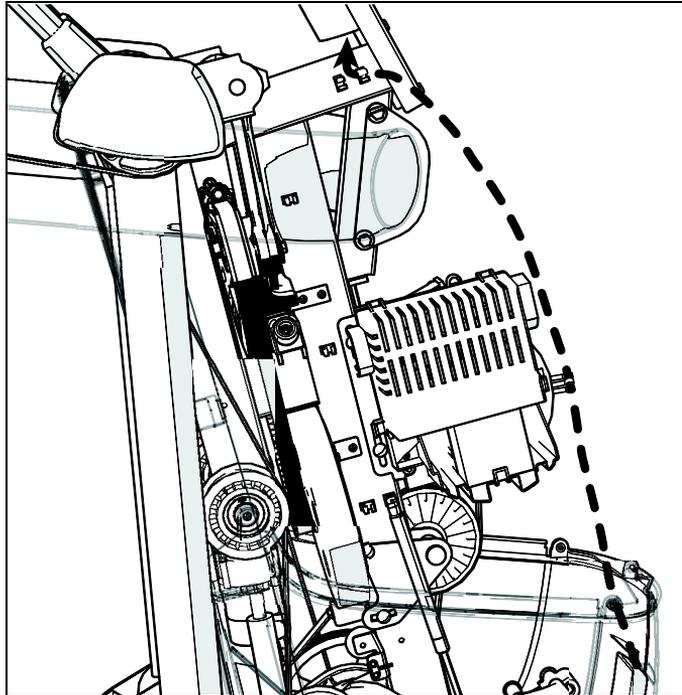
Recorrido del cable a través de la estructura hacia la columna central
